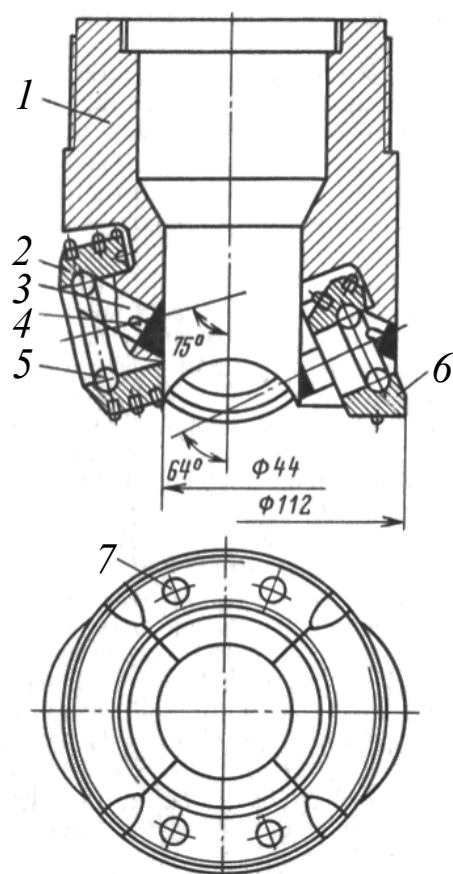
Конструкция шарошечной коронки БДК 112К: 1 – корпус кольцевой формы; 2 – внутренняя шарошка (формирующая керн); 3 – замковый палец; 4 – штифт-фиксатор; 5 – замковый шариковый подшипник; 6 – наружная шарошка (формирующая ствол скважины); 7 – циркуляционные каналы
